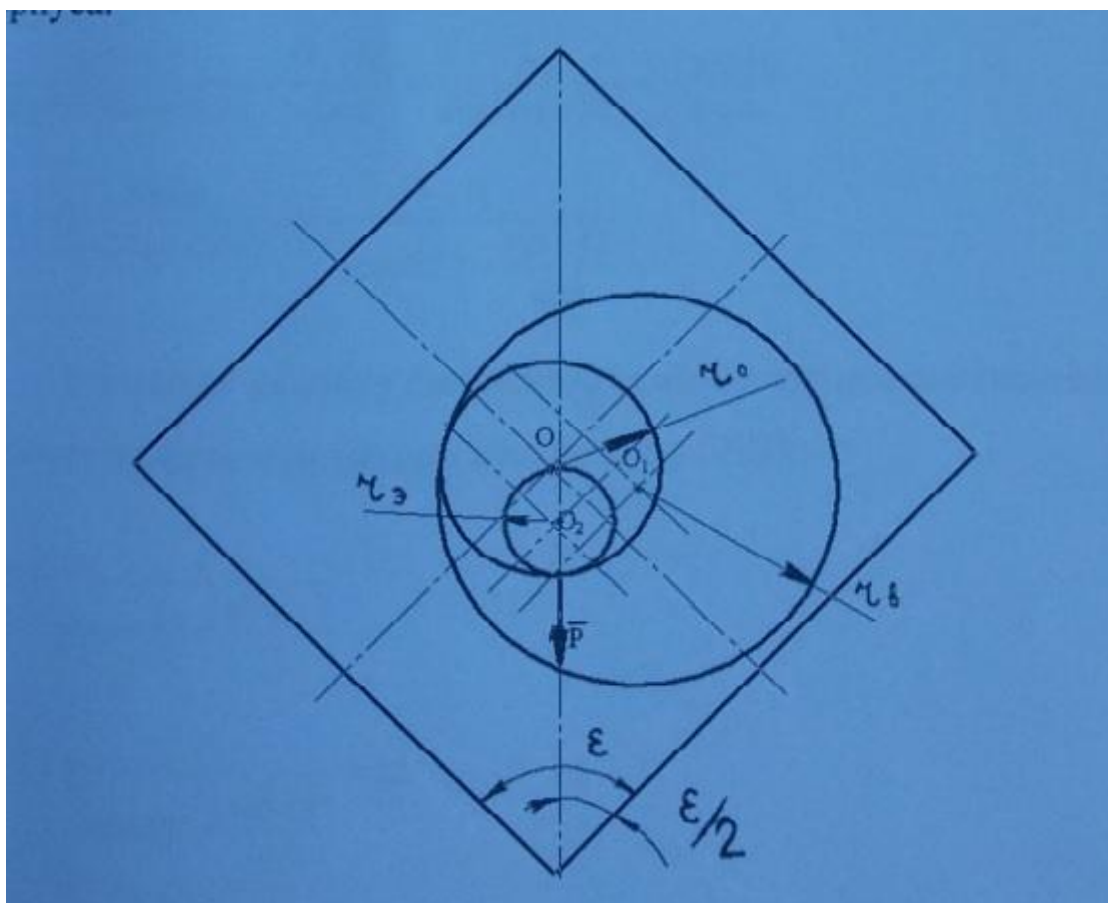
Расчетная схема эксцентрического закрепления.
